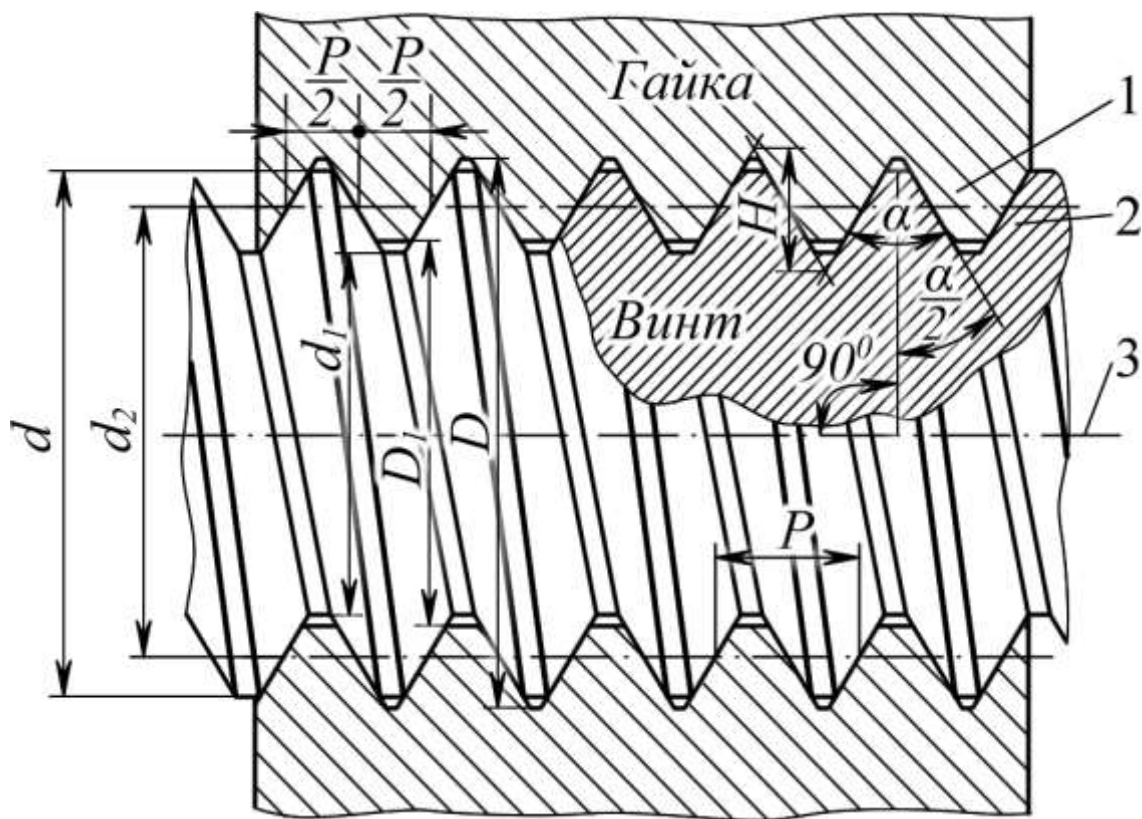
Профиль резьбы в соединении винт-гайка:
